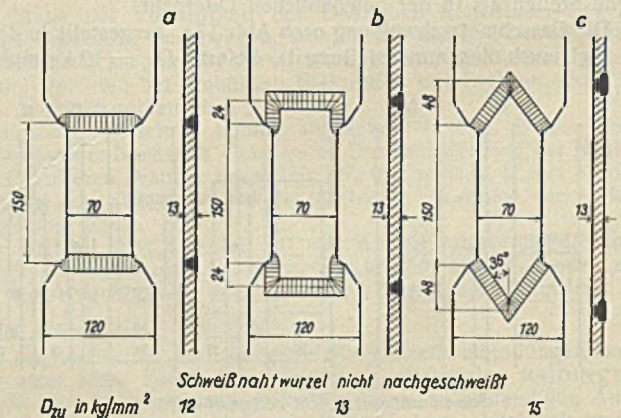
a bis c. Dauerzugversuche mit Gasschmelzschweißungen; Knotenblechanschlüsse, St 37.
